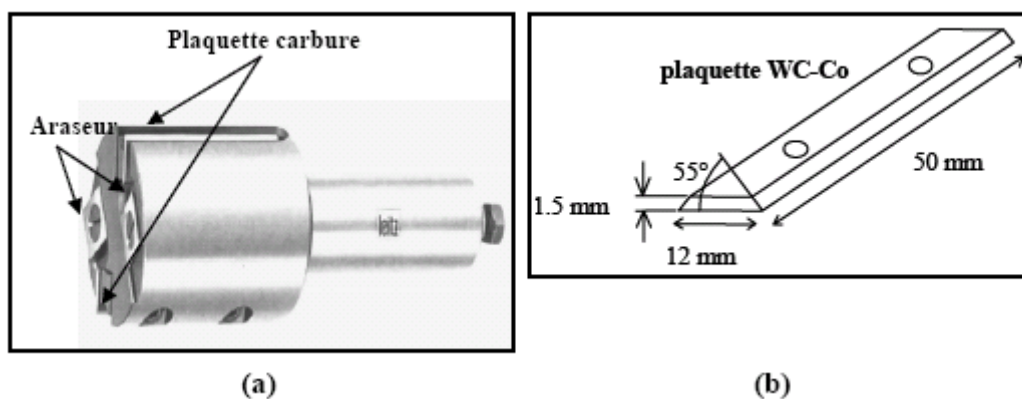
(a) Outil de fraisage (défonçage), (b) géométrie des plaquettes carbures
